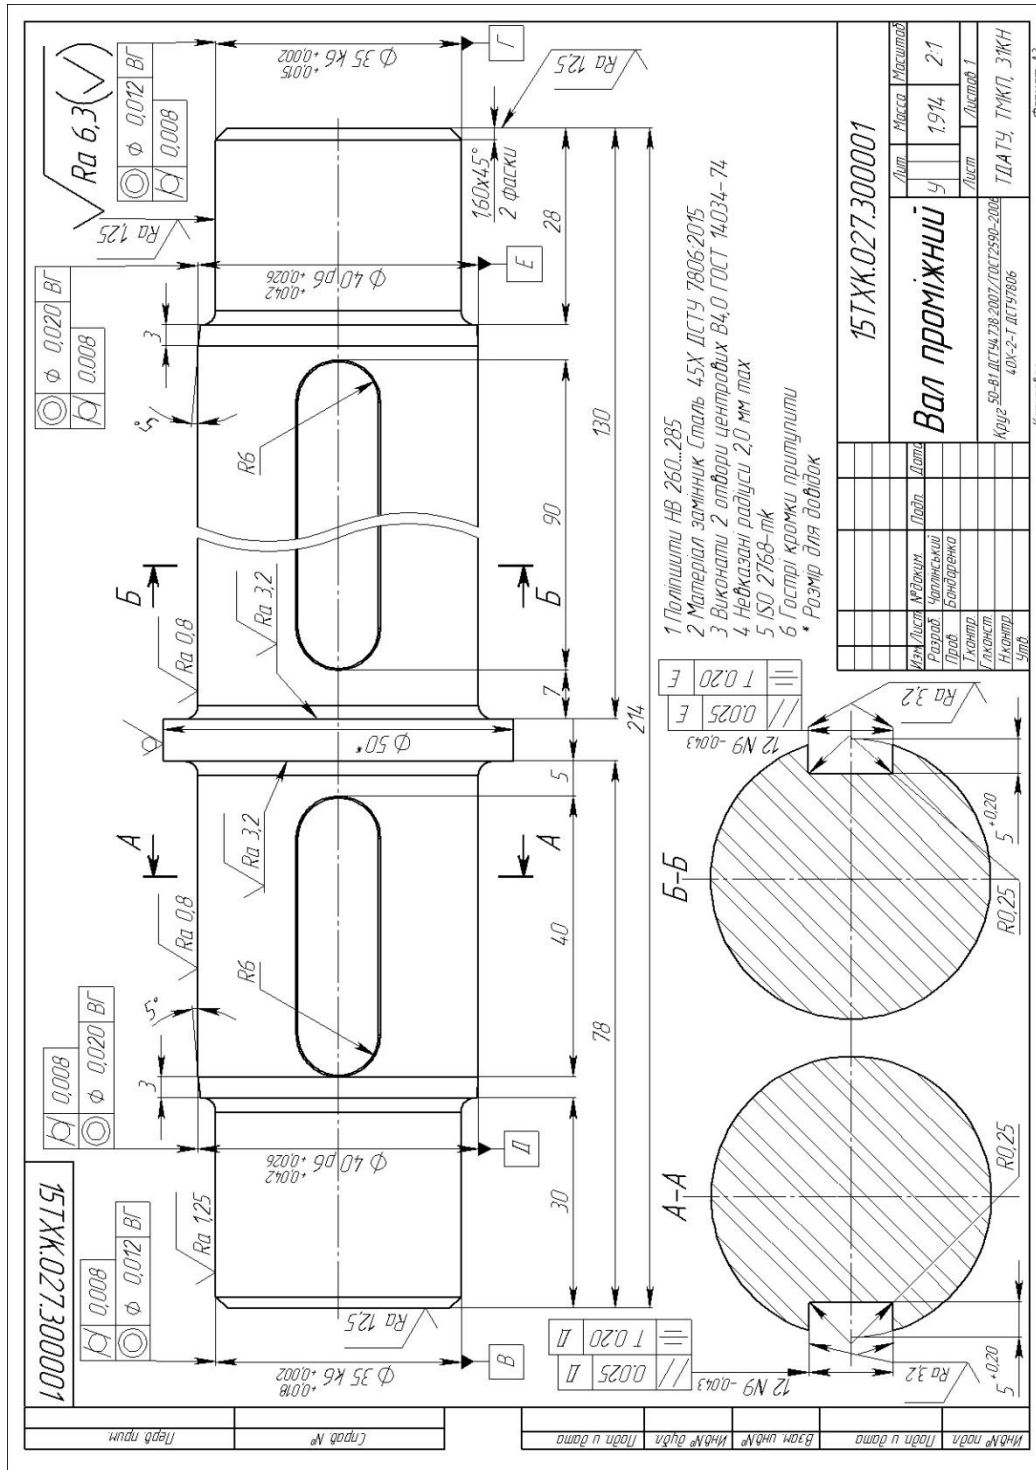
Розташування допусків форми та розташування поверхонь.
